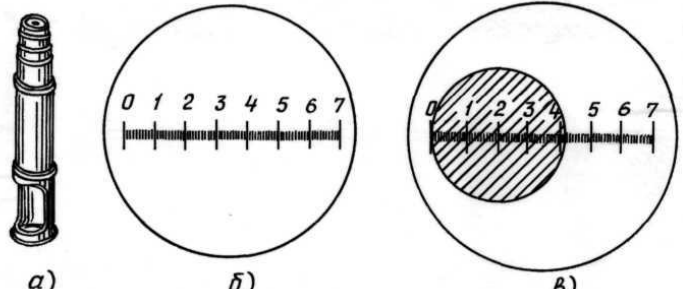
Лупа для измерения отпечатков: а - внешний вид; б - шкала лупы; в - отпечаток на шкале лупы
